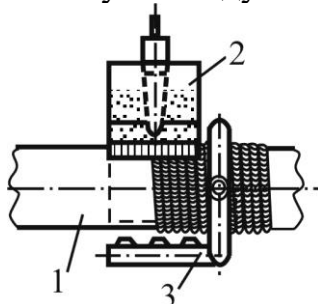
Схема вибродуговой наплавки под флюсом
